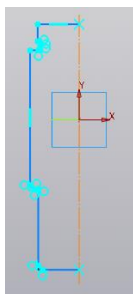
Эскиз вертикальной цилиндрической части корпуса
